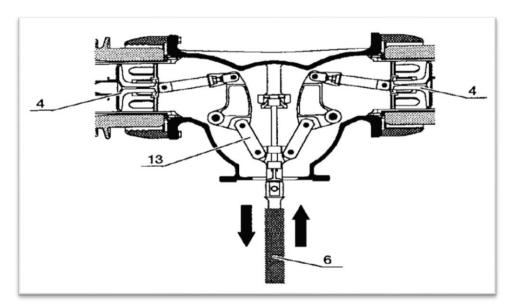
PARTES DEL CARTER SUPERIOR.
